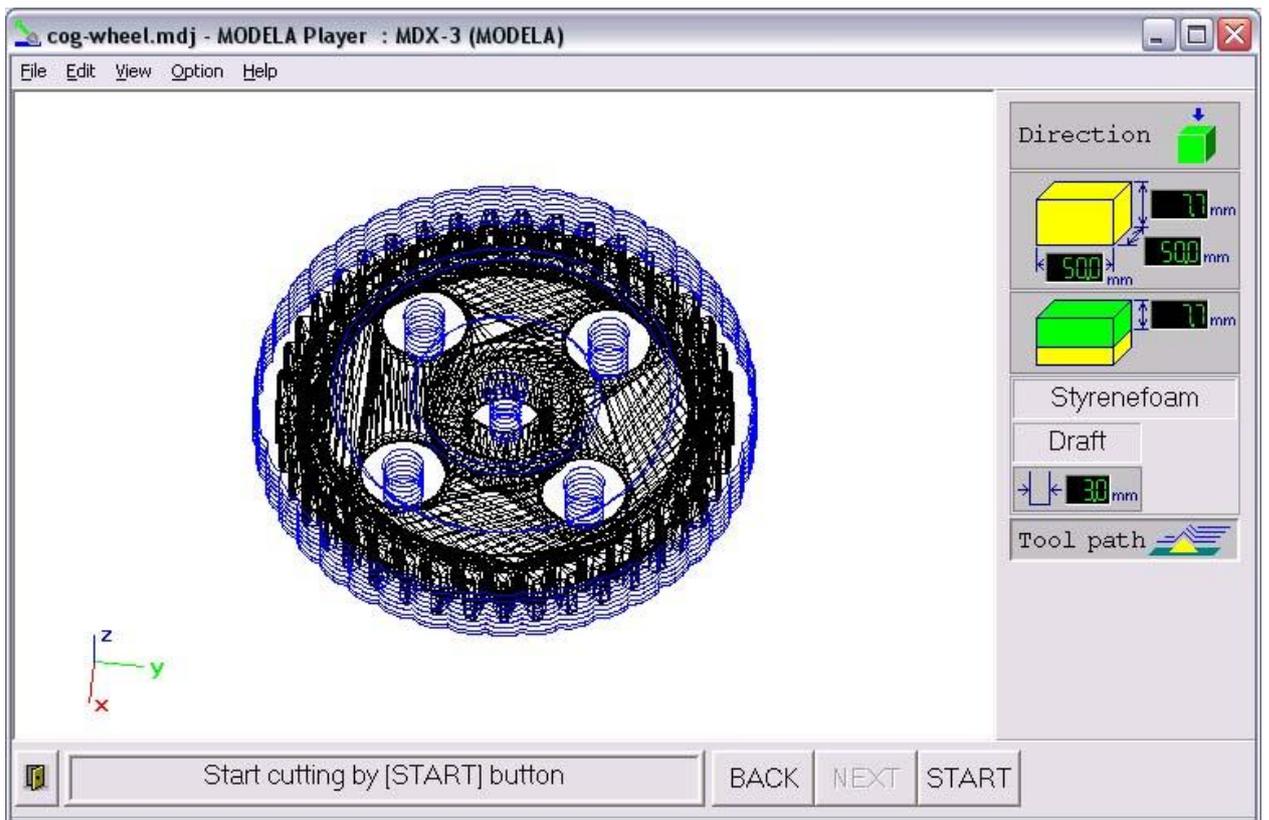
Траектория движения инструмента при изготовлении зубчатого колеса
